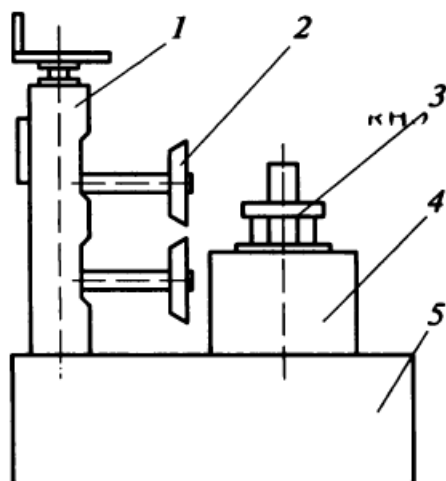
Схема станда 1102 для демонтажных работ шин:
